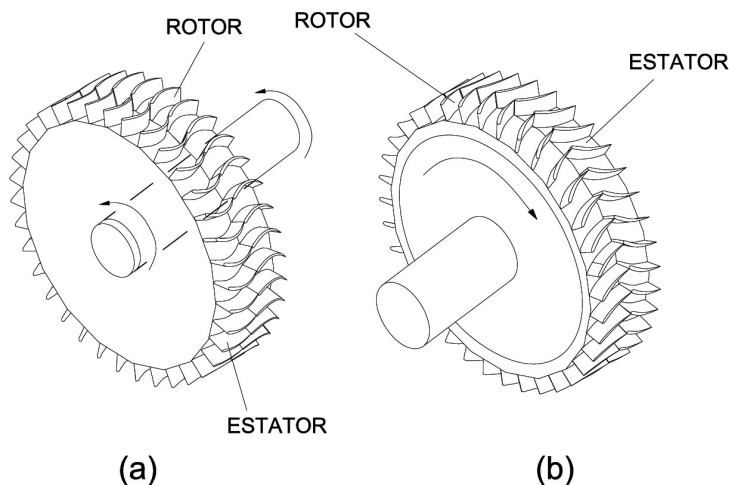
a) turbina elemental axial y b) turbocompresor elemental axial.
